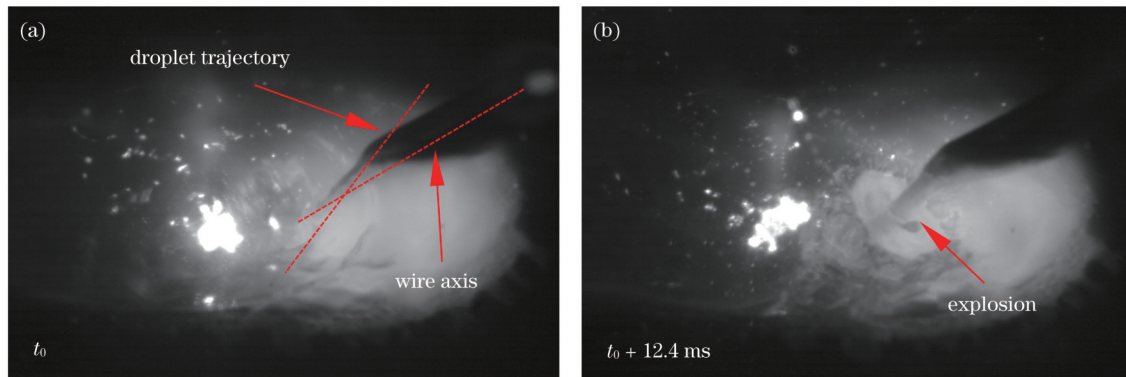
焊接过程中的高速摄像照片(4#试验)
